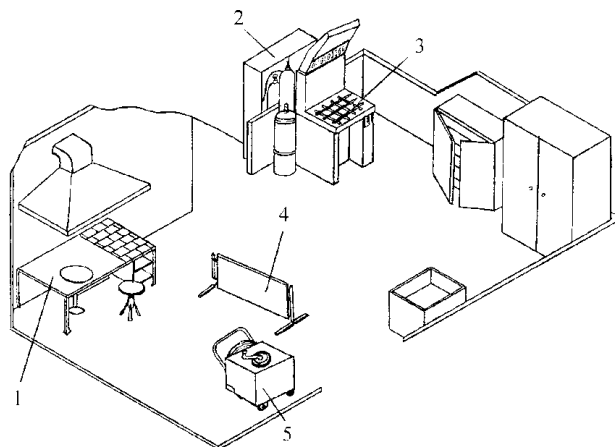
Дільниця газоелектрозварювання: 1 – стіл для електрозварювальних робіт ОКС-7523; 2 – шафа для зберігання балонів з киснем і ацетиленом ОРГ-5127; 3 – стіл для газозварювальних робіт з
